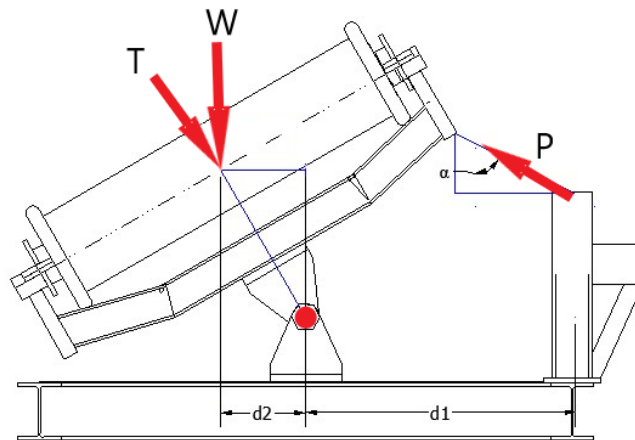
Fuerzas aplicadas sobre el sistema elevador. Siendo P , la fuerza necesaria que requiere para operar el cilindro hidráulico.
